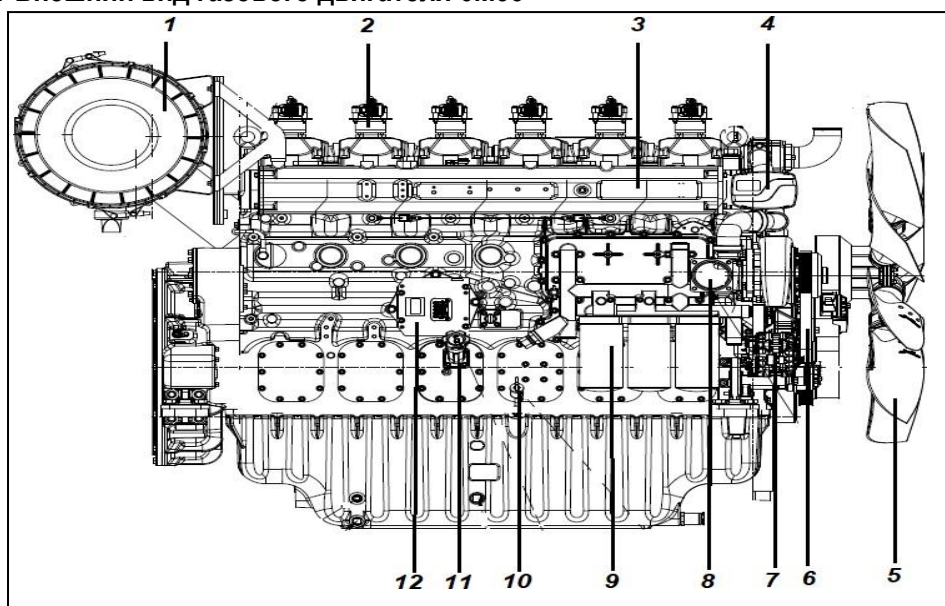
А – Вид двигателя со стороны впускного коллектора
